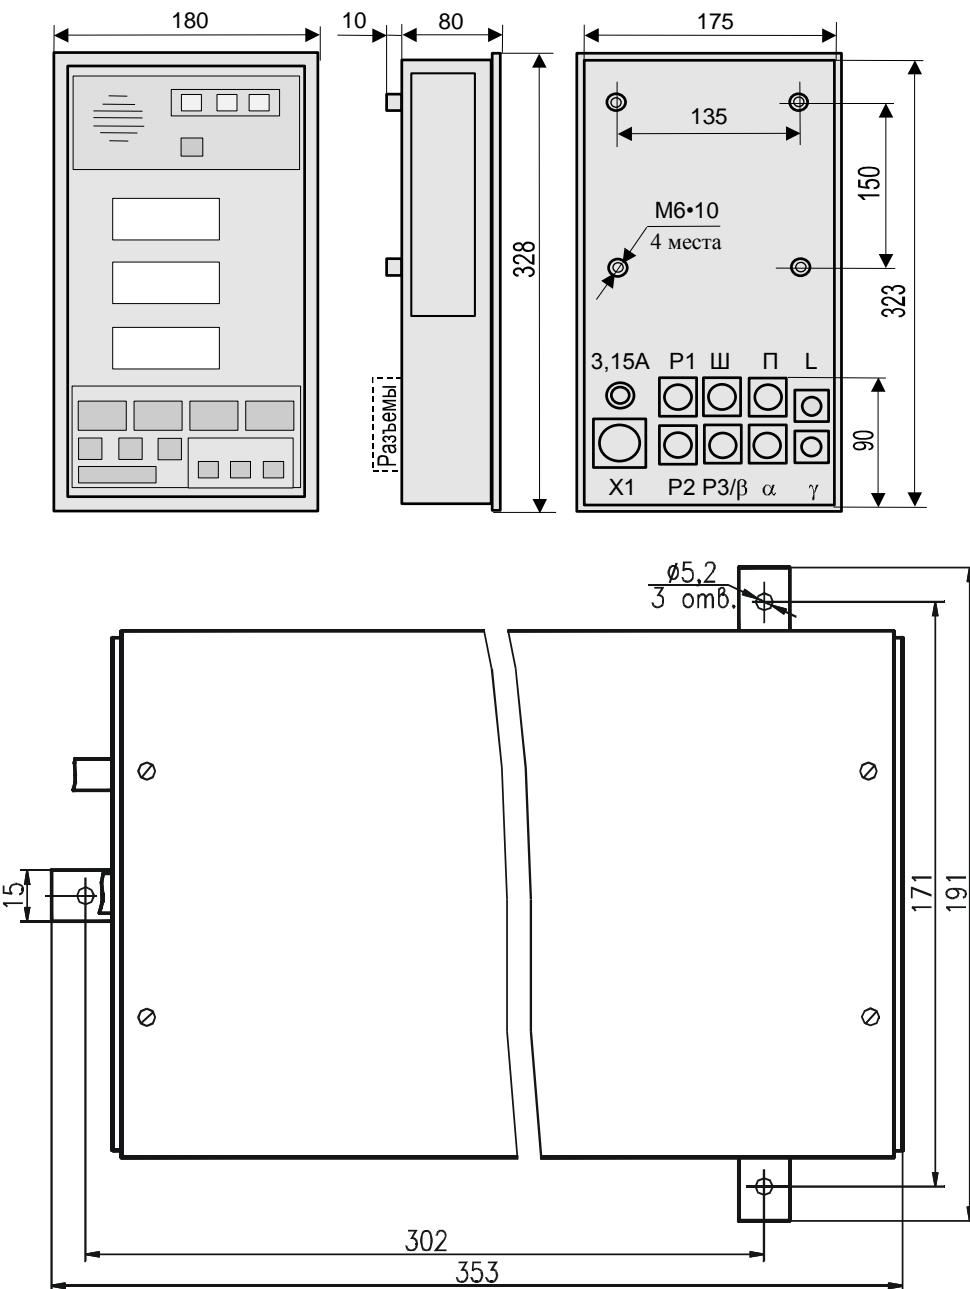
Габаритные и присоединительные размеры БОД и БПВР
